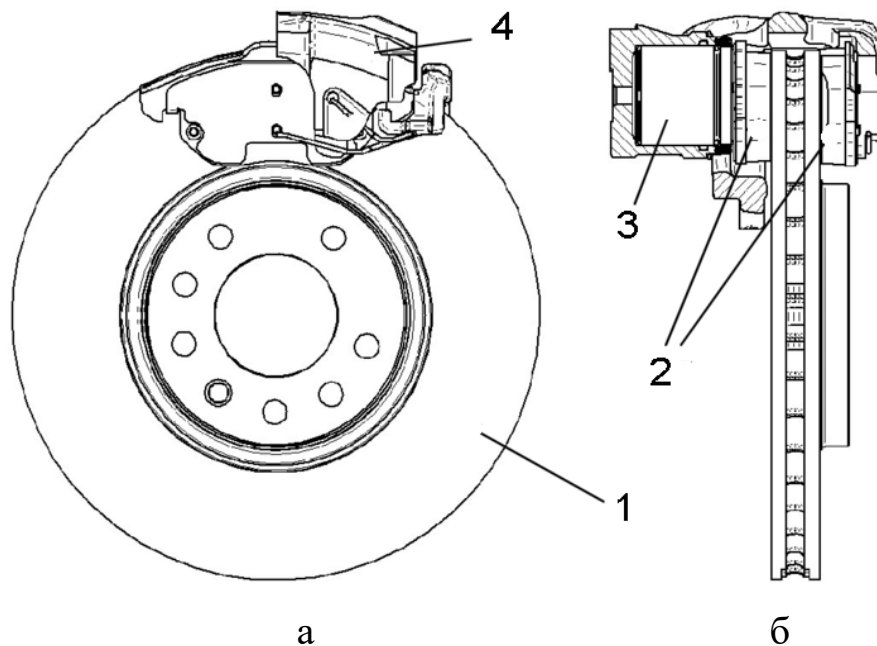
Загальна схема конструкції дискового гальмівного механізму:
